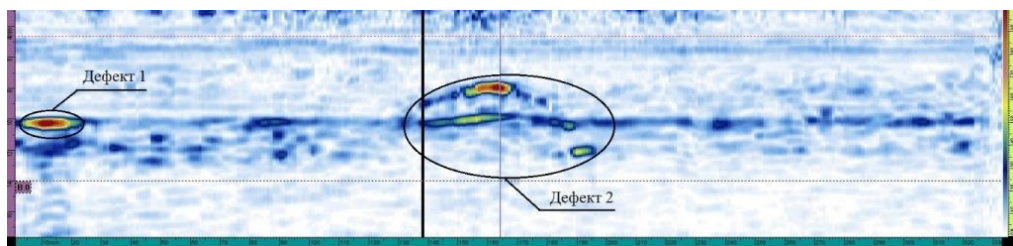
Схема расположения сканов различного сварных соединений.
